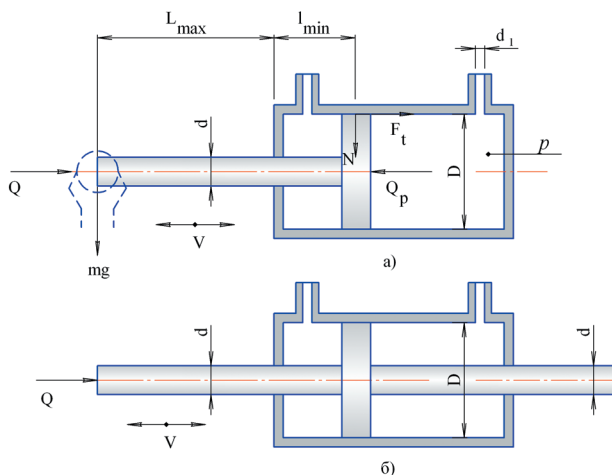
Розрахункова схема поршневого пневматичного приводу
